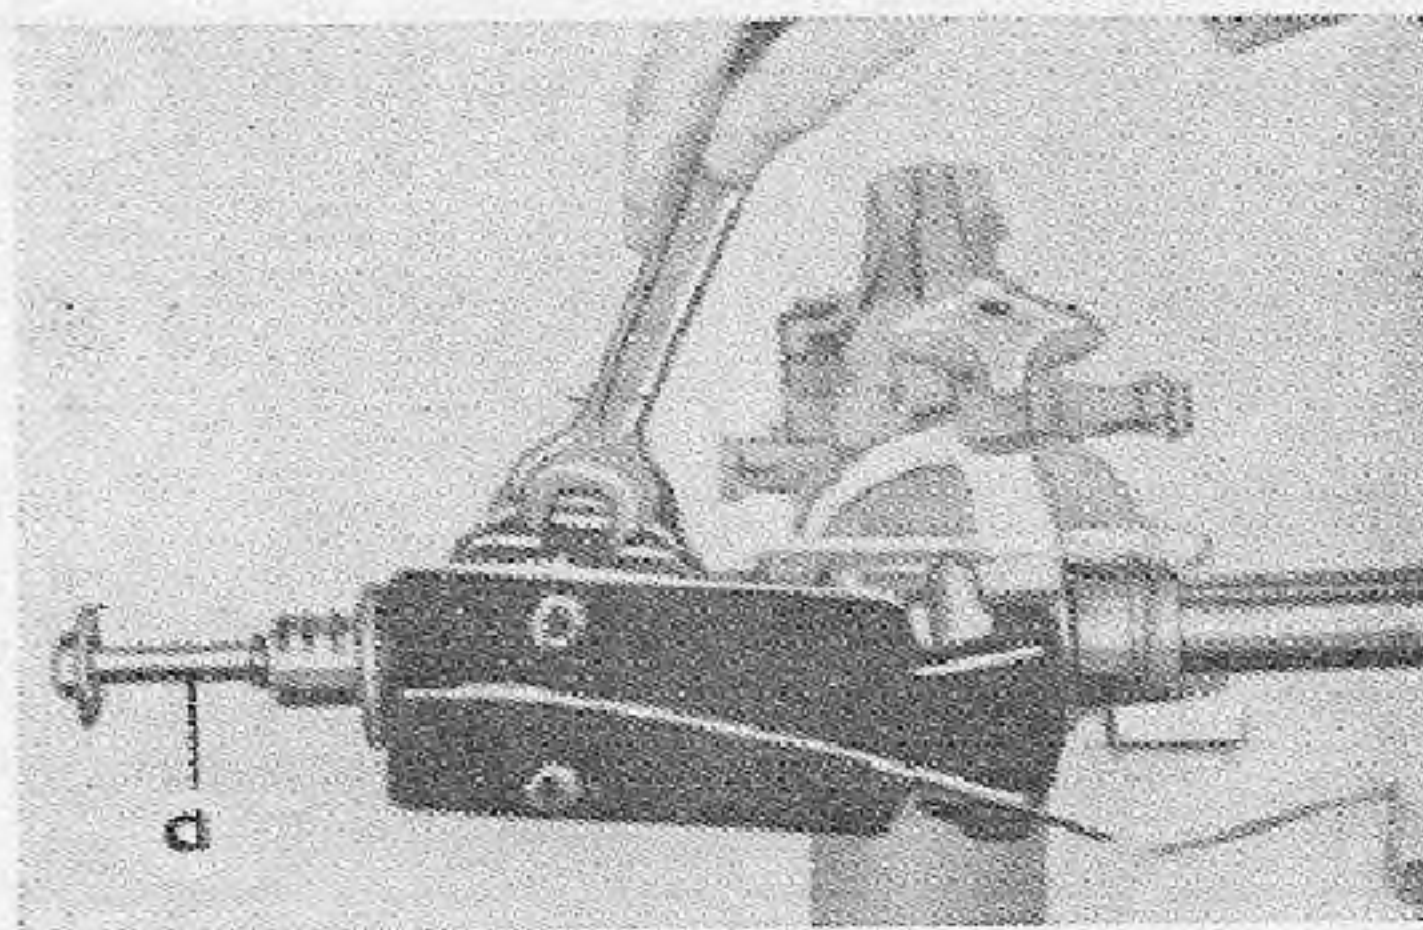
Ajuste del par motor con el dispositivo DK 114.
